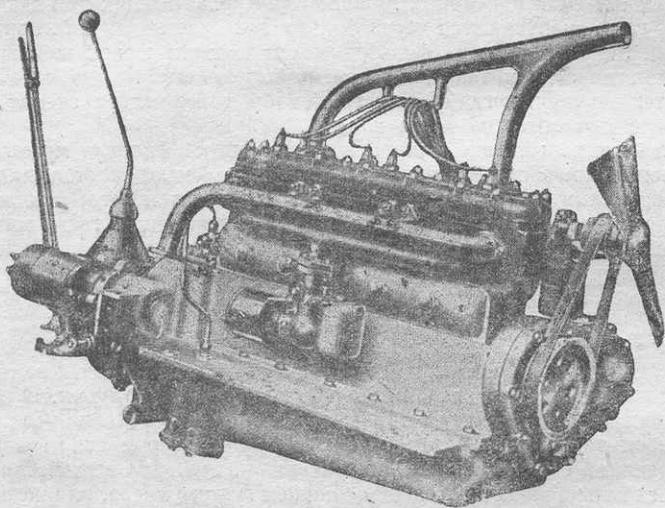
Двигатель с коробкой передач автомобиля НСУ, 7/34 л. с.
